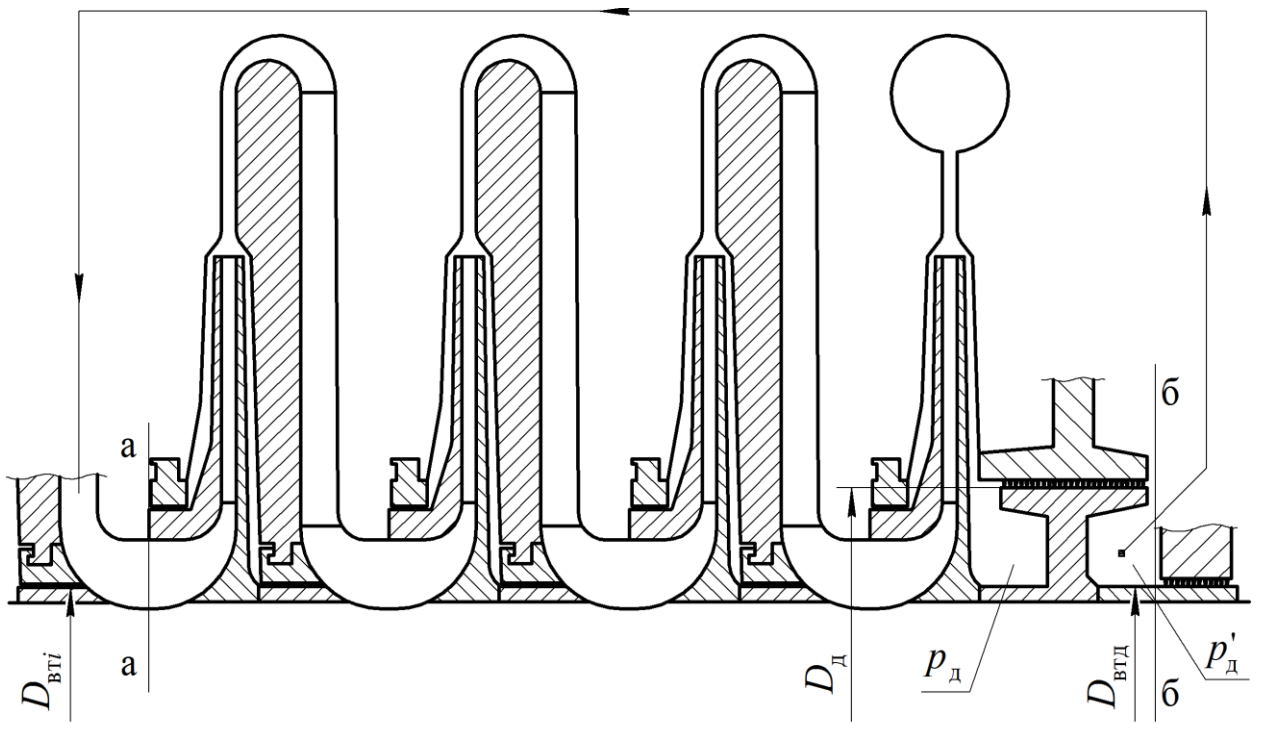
Схема ротора с односторонним расположением рабочих колес
